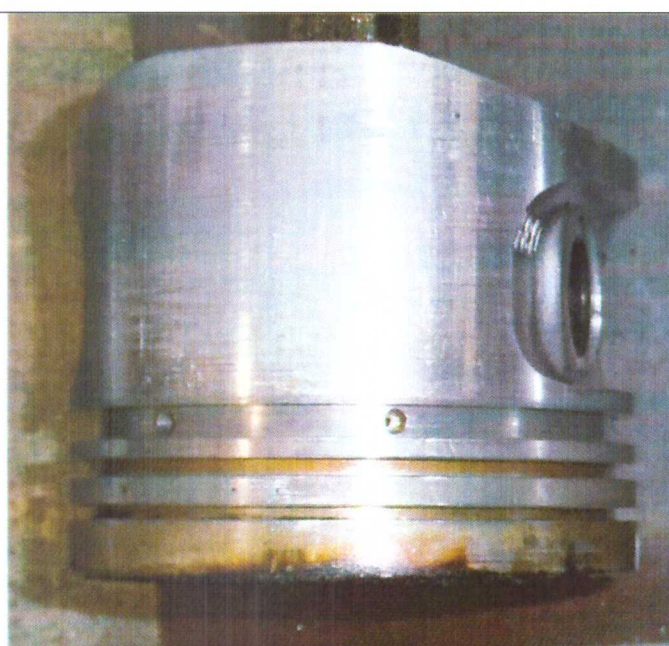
Внешний вид боковой поверхности поршня четвертого цилиндра по окончании длительных испытаний двигателя при работе на базовом масле Castrol EDGE с добавкой нанокompозита Amortect PROOF
